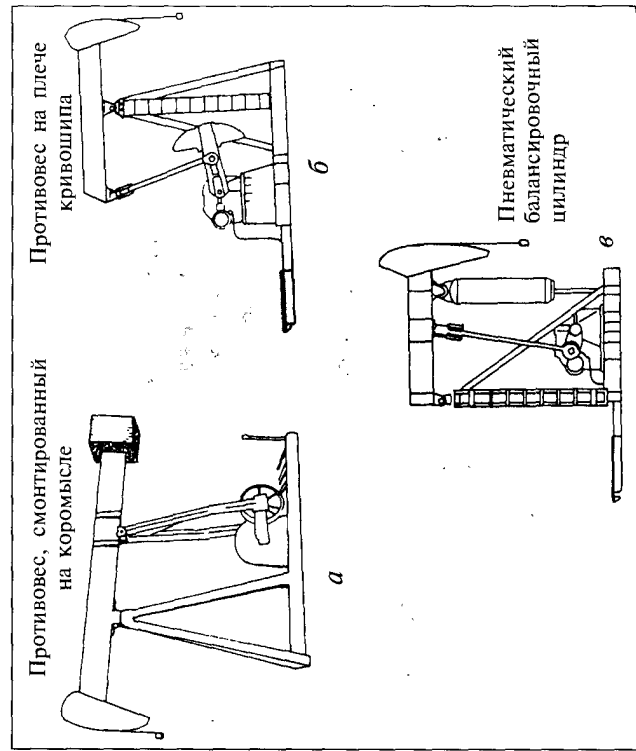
Типы балансировки качалок: а — коромысловая, б — кривошипная и в — пневматическая
